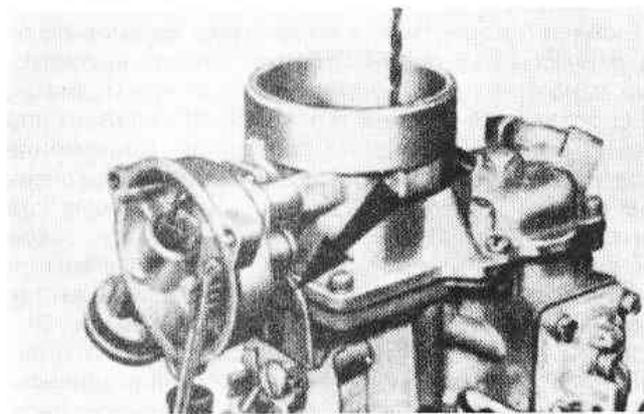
Точка регулировки метки "V" (Разд.24)
